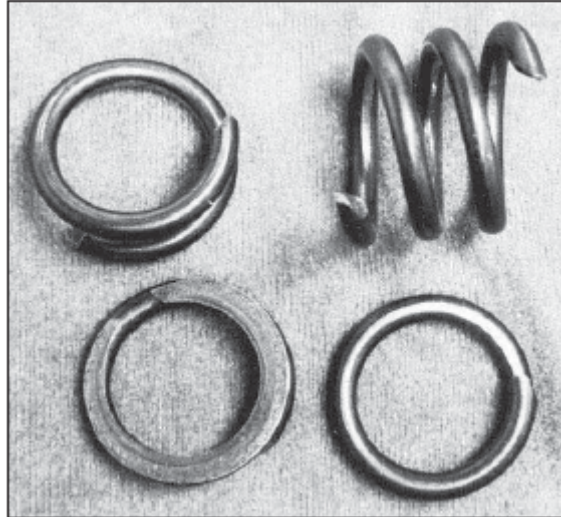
Rotura de un resorte de válvula en un motor sobrerrevolucionado
